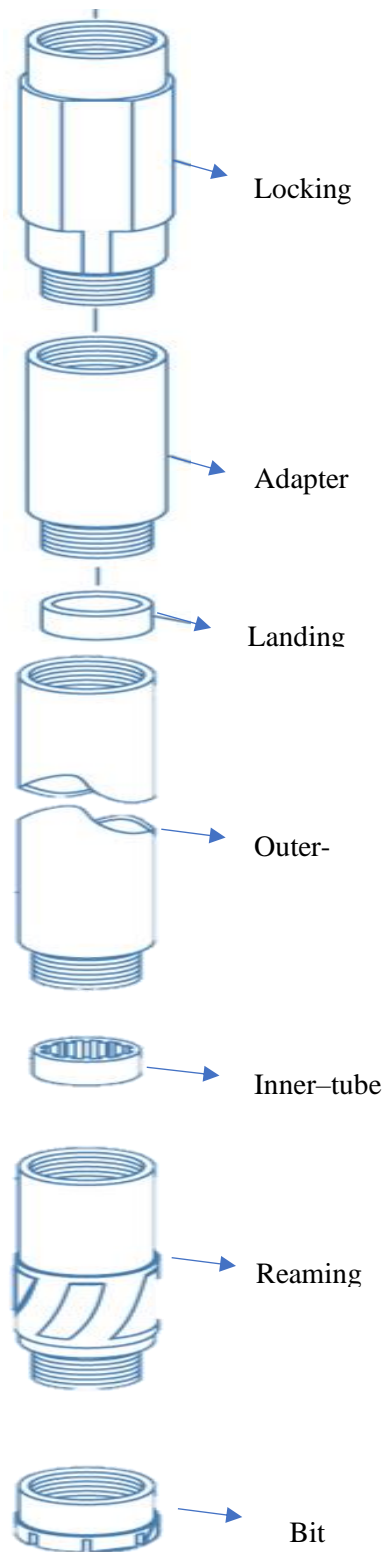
Despiece de Barel. Tomada de «Productos BWL V-Latch Core Barel Assembly», por Hole productos. 2022.
